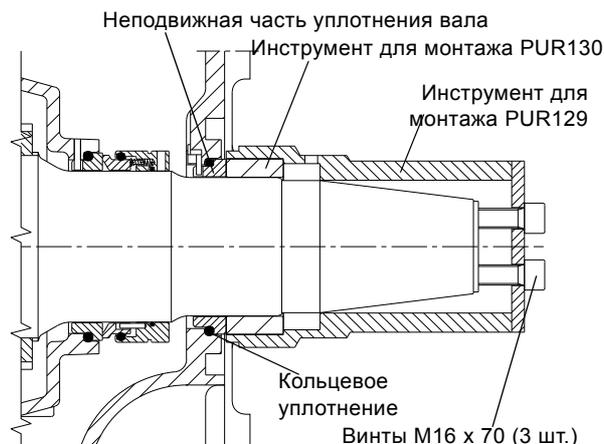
Установка неподвижной части первичного уплотнения вала, типоразмер 78
